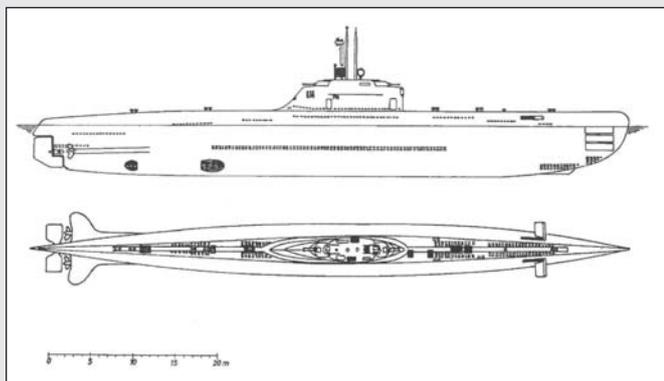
Alzado y planta del proyecto XVIII de submarino con propulsión Walter - Diesel
